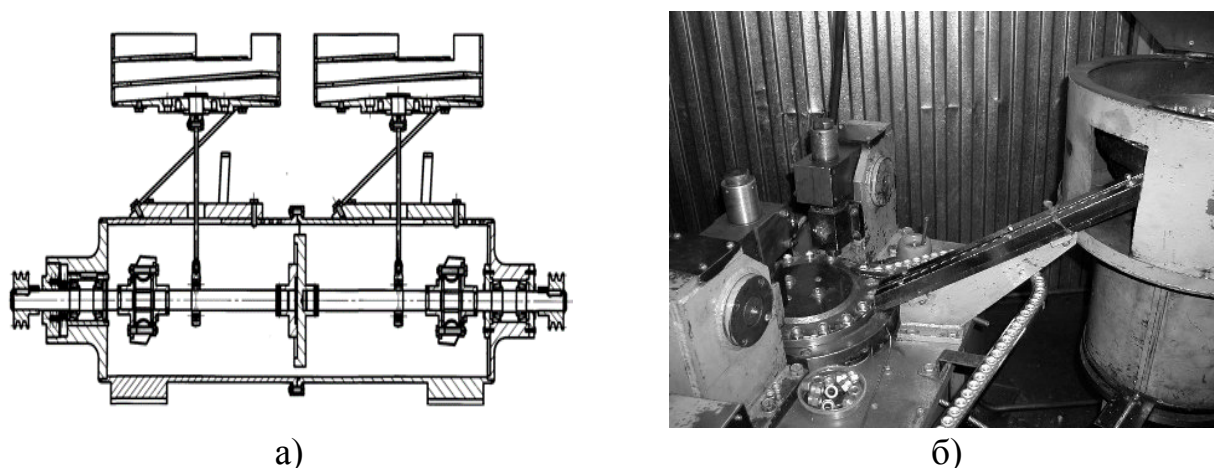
Вибрационный бункерный питатель: а) схема; б) общий вид
